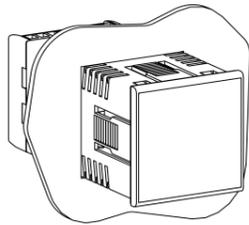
Монтаж прибора щитового крепления Щ5
